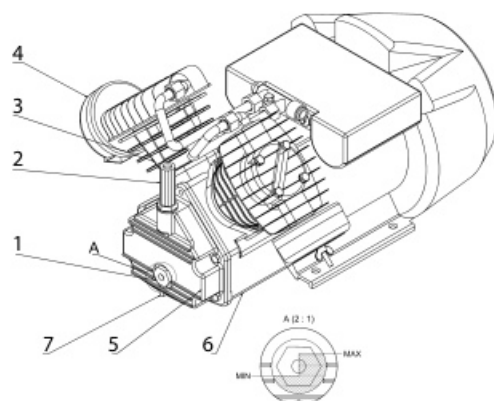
Устройство внешних узлов поршневого блока компрессоров BCD-50-400, BCD-100-400
